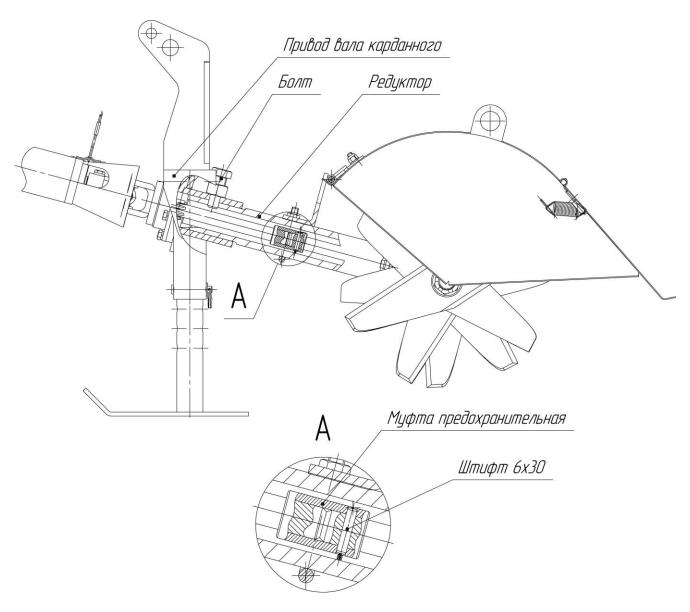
Предохранительная муфта в редукторе фрезы почвообрабатывающей ФР-00.700-Б.
